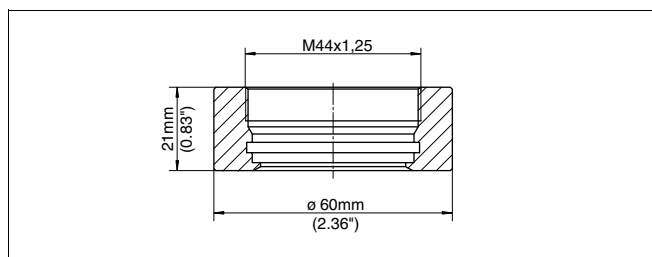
Medidas da luva soldada M44 x 1,25
